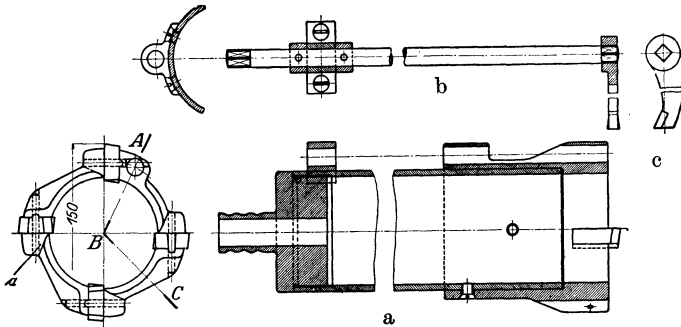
Hohlbohrer mit Einstechvorrichtung.
